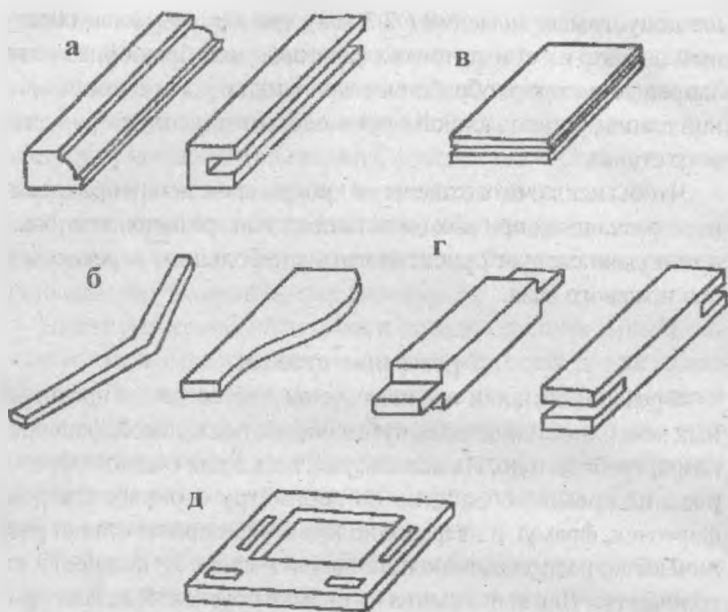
Виды обработки на фрезерных станках: а-продольное профильное фрезерование; б-криволинейное фрезерование; в-обработка по контуру; г-фрезерование шипов; д-профильное фигурное фрезерование
